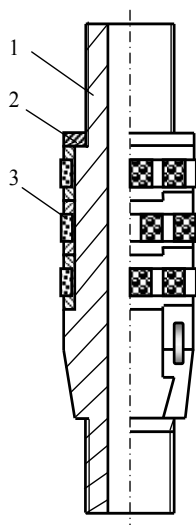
Калибратор КАНБ: 1 – корпус; 2 – зажимная шайба; 3 – кольцо с алмазосодержащими штабиками
